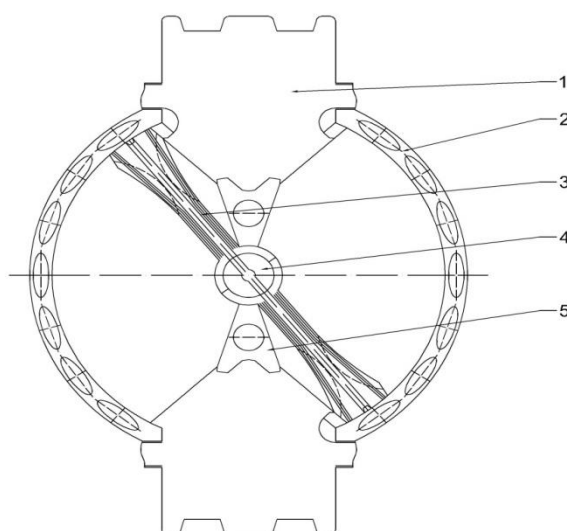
Схема предлагаемой конструкции лопастного двигателя: 1 – газораспределительный механизм; 2 – корпус двигателя; 3 – рабочая лопасть; 4 – вал лопасти; 5 – разделительная перегородка
